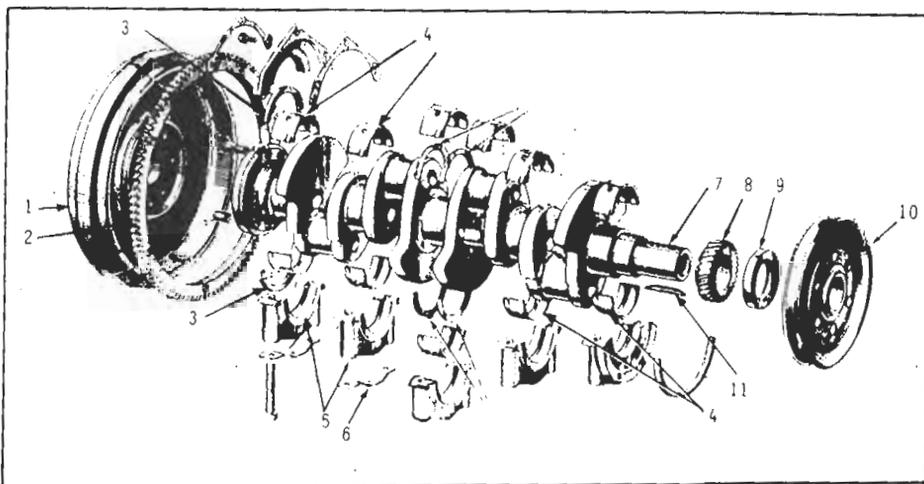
Despiece volante, cigüeñal y polea (FORD). 1.- Volante. 2.- Corona dentada para el motor de arranque. 3.- Retén de aceite. 4.- Casquillos antifricción. 5.- Sombreretes de biela. 6.- Frenillo de seguridad. 7.- Cigüeñal. 8.- Piñón de mando de la distribución. 9.- Retén de aceite. 10.- Polea de la correa del ventilador. 11.- Chaveta.
